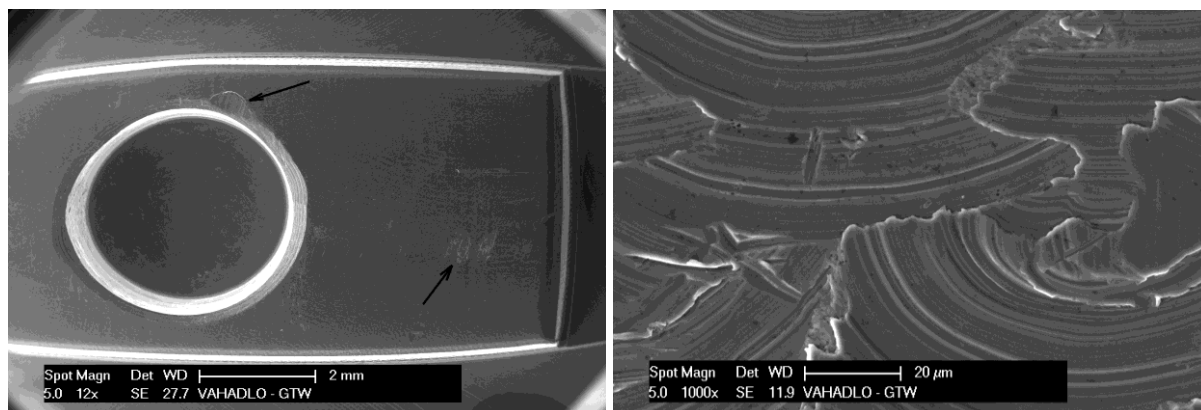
Povrchový stav v místě 2 (vlevo); Povrchový stav v místě 2 – detail (vpravo)
